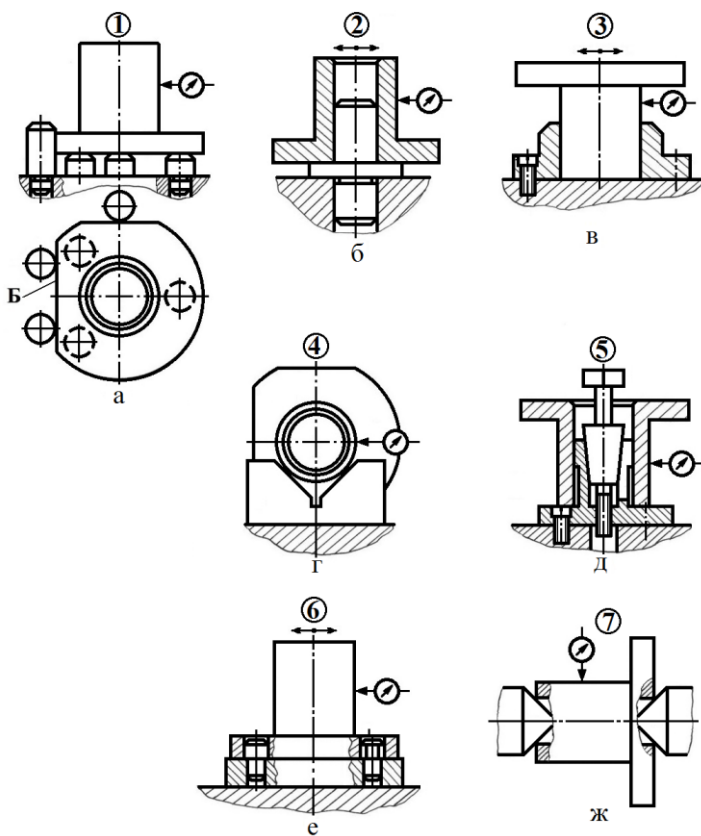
Схемы базирования и замера погрешностей для различных вариантов установки образца
